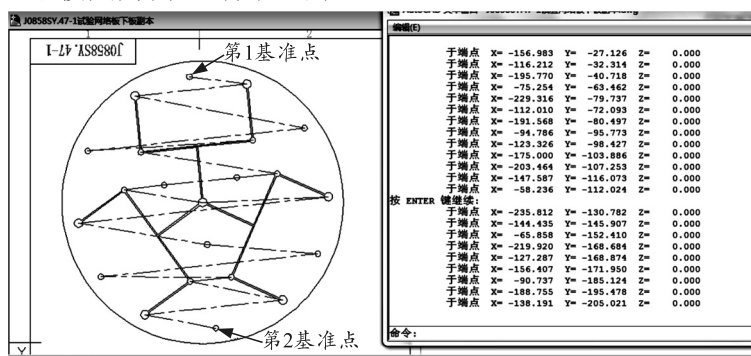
CAD 图纸中各挤注点位置坐标生成窗口
